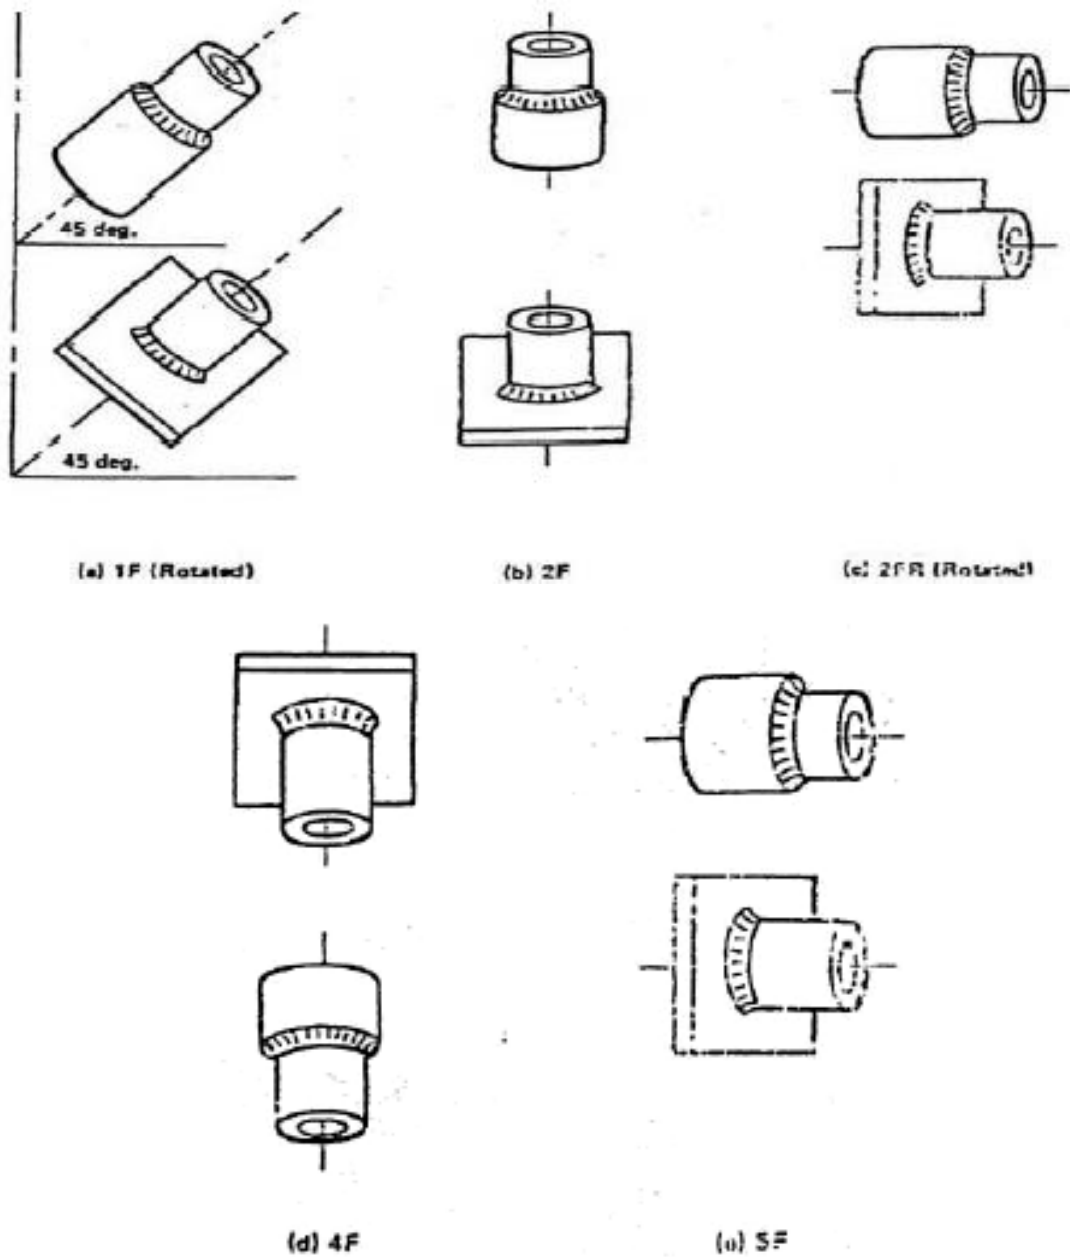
POSICIONES DE SOLDADURA EN TUBO CON SOLDADURA DE FILETE (Ref. 5)
